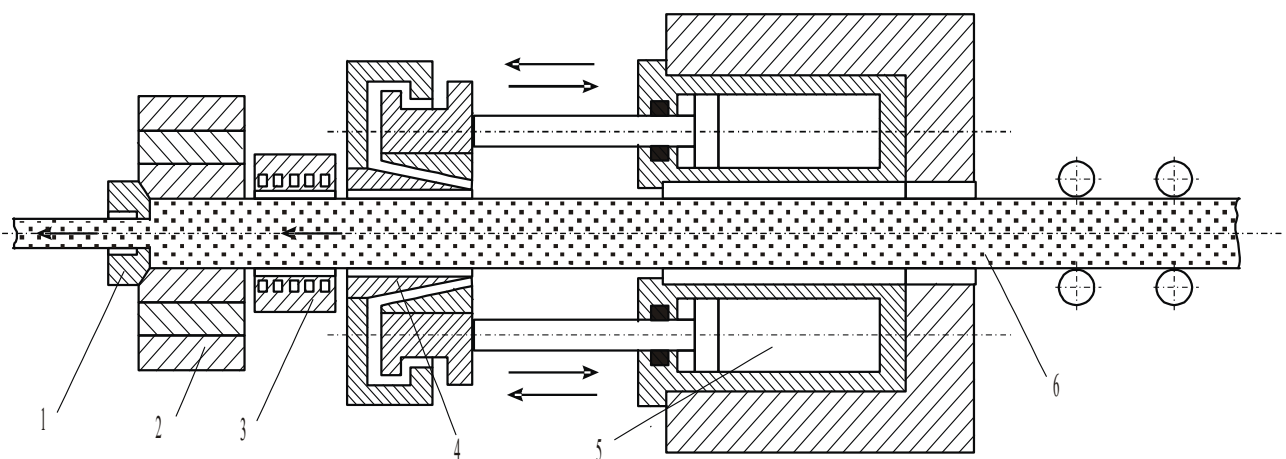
Схема агрегату для безперервного пресування литому заготовки необмеженої довжини: 1 – матриця; 2 – контейнер; 3 – індуктор; 4 – затискач заготовки; 5 – циліндри робочого ходу; 6- заготовка
